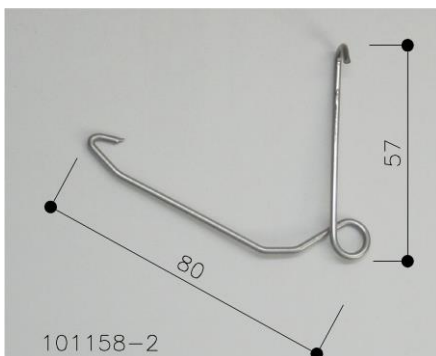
voorbeeld voor Belux: E-clips type 2 panhaak betondakpan
